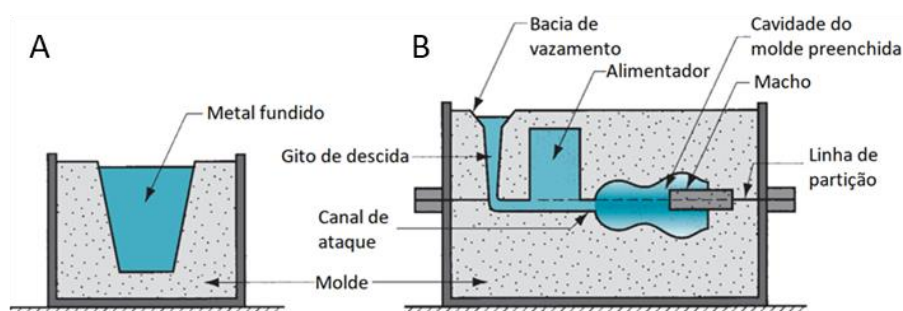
Moldação em céu aberto (A) e moldação fechada (B) (adaptado de [8]).
